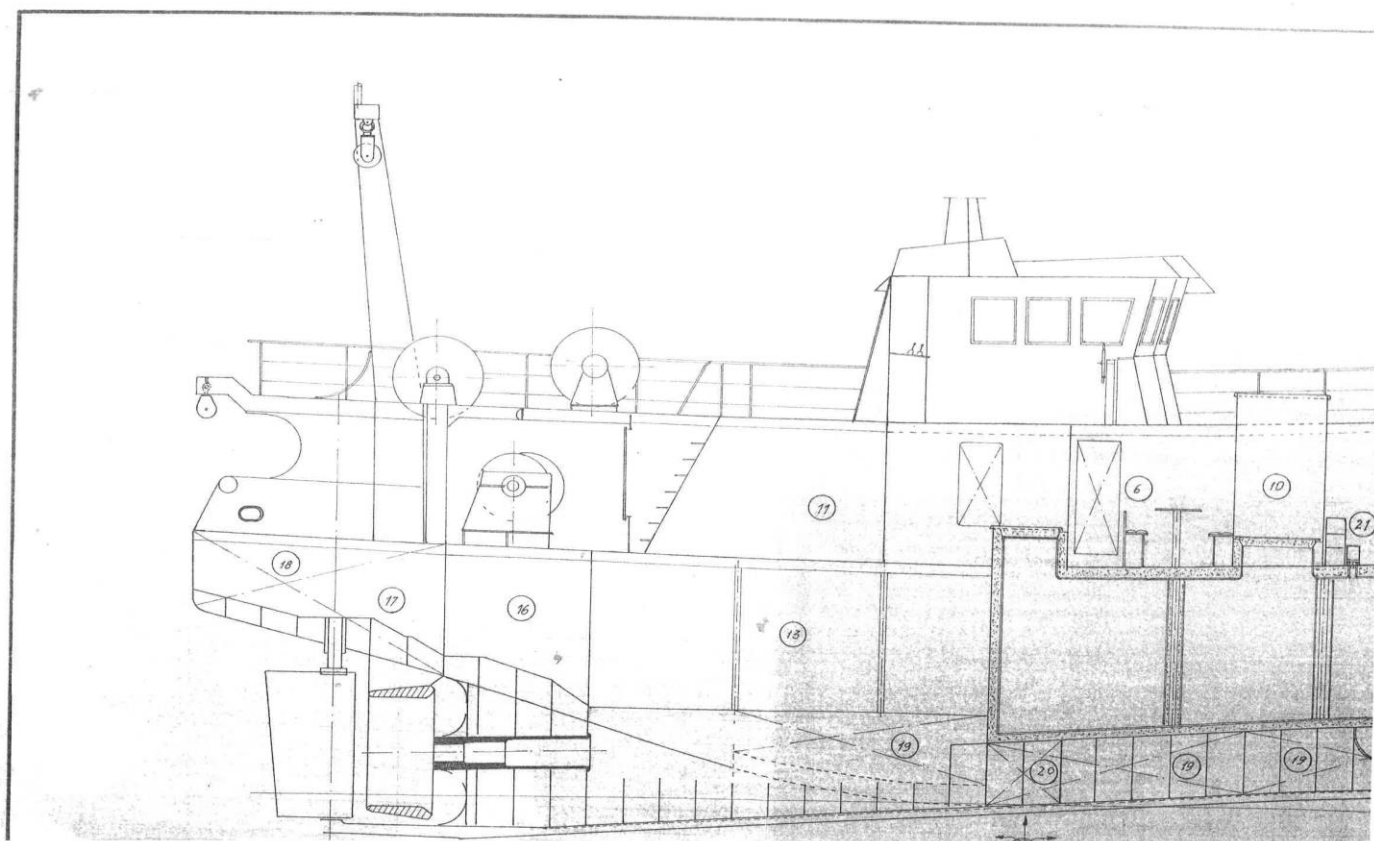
Pormenor do arranjo geral da embarcação OLIVIA RIBAU
